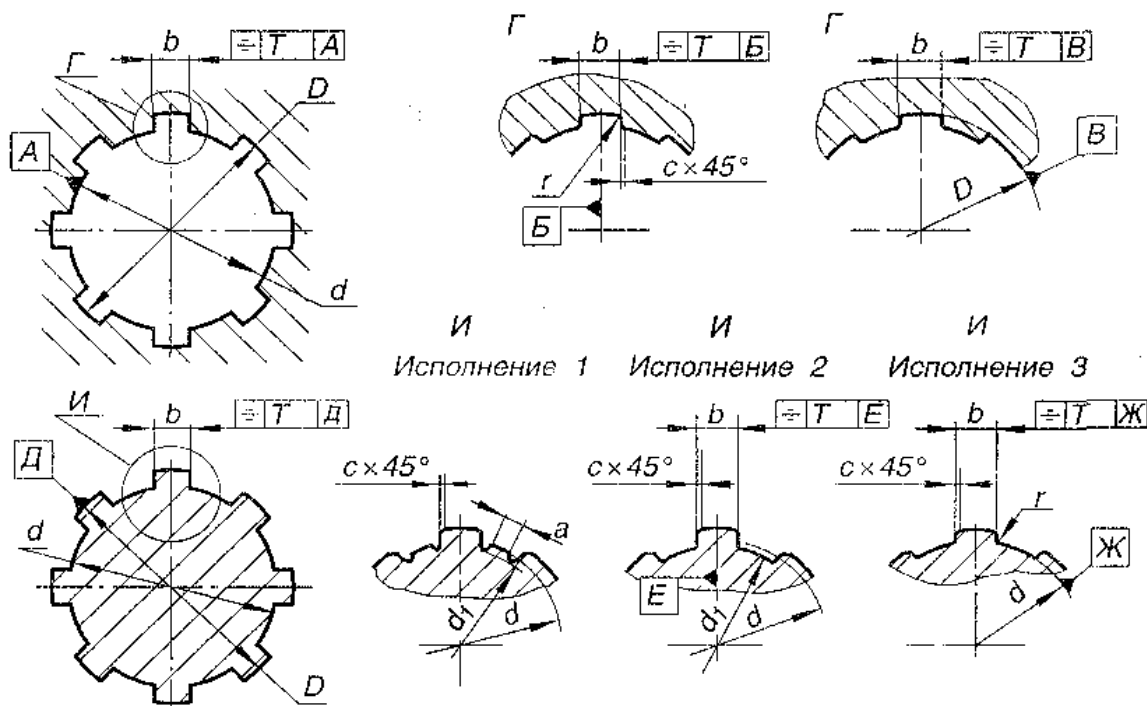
Размеры основных параметров и число зубьев шлицевых соединений
